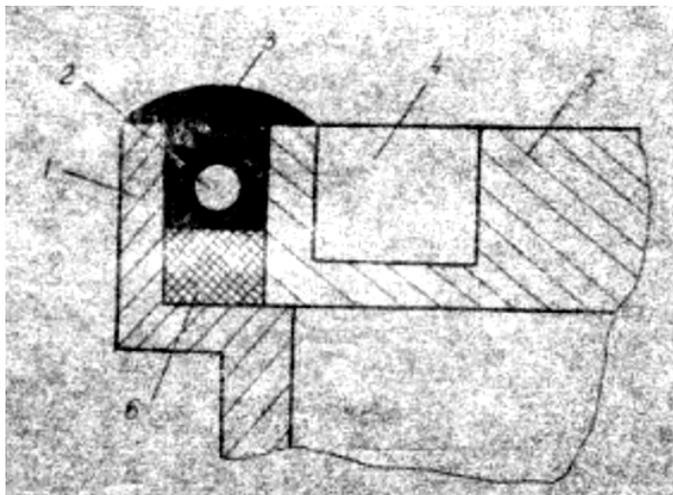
Герметизация корпуса паяным швом: 1 - корпус,
